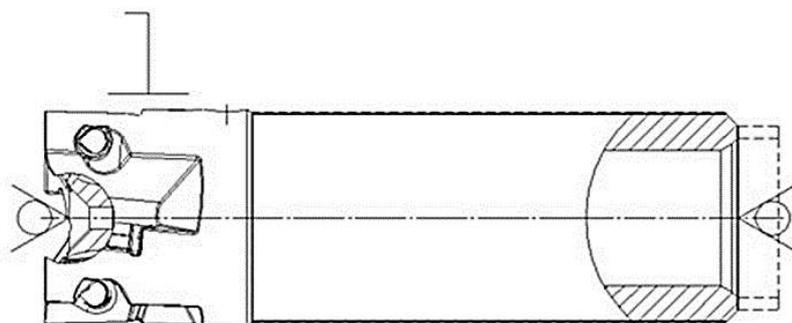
Схема базирования детали при обработке базовых цилиндрических поверхностей
